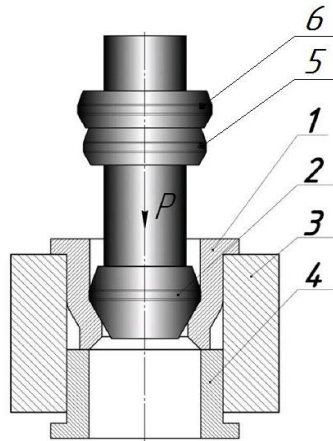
Схема способа изготовления втулок с концевым утолщением: 1-заготовка; 2,5,6-соответственно первый, второй и третий зубья дорна; 3-обойма; 4-опорная втулка
